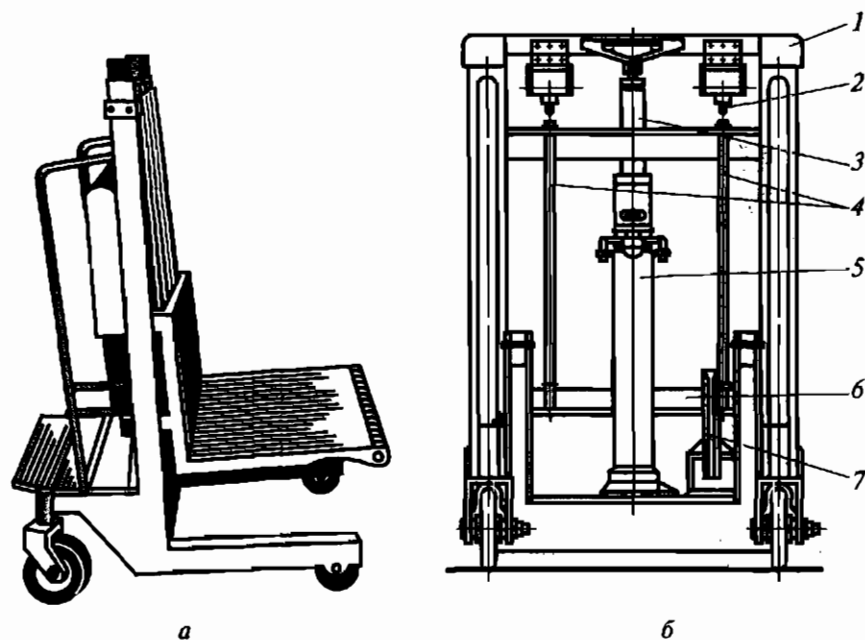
Общий вид (а) и устройство (б) гидравлического подъемника:
